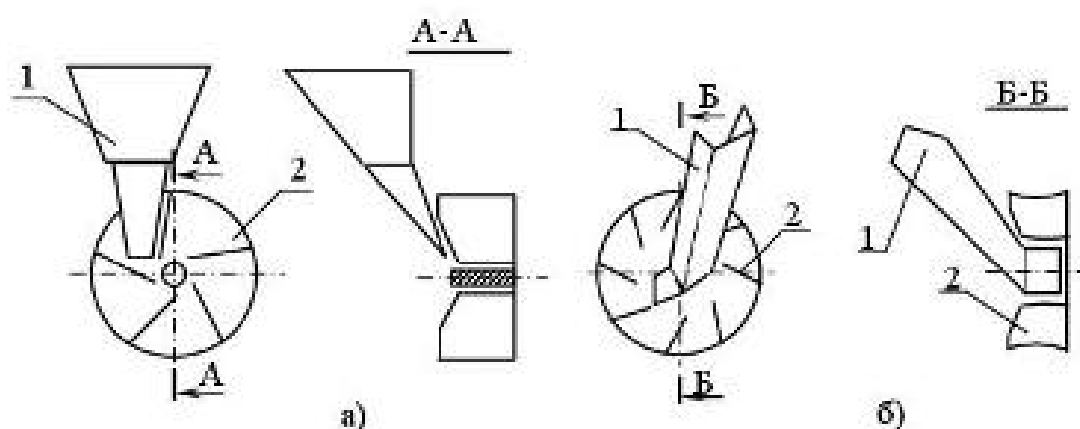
Схемы способов подачи зернового вороха на лопатки диска метателя
